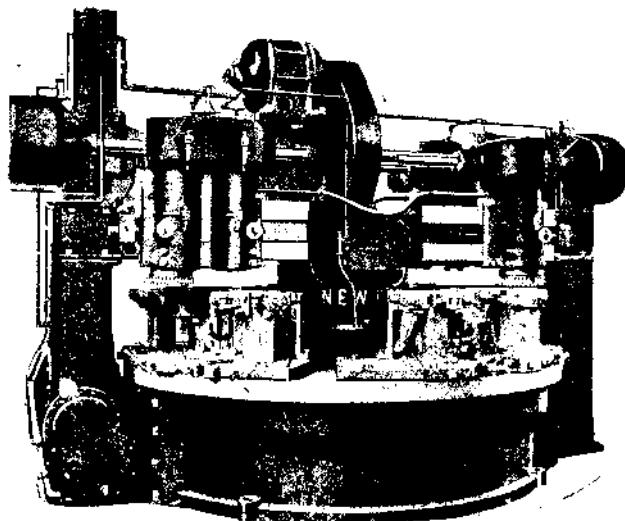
Станок Ньютон для непрерывного фрезерования.
